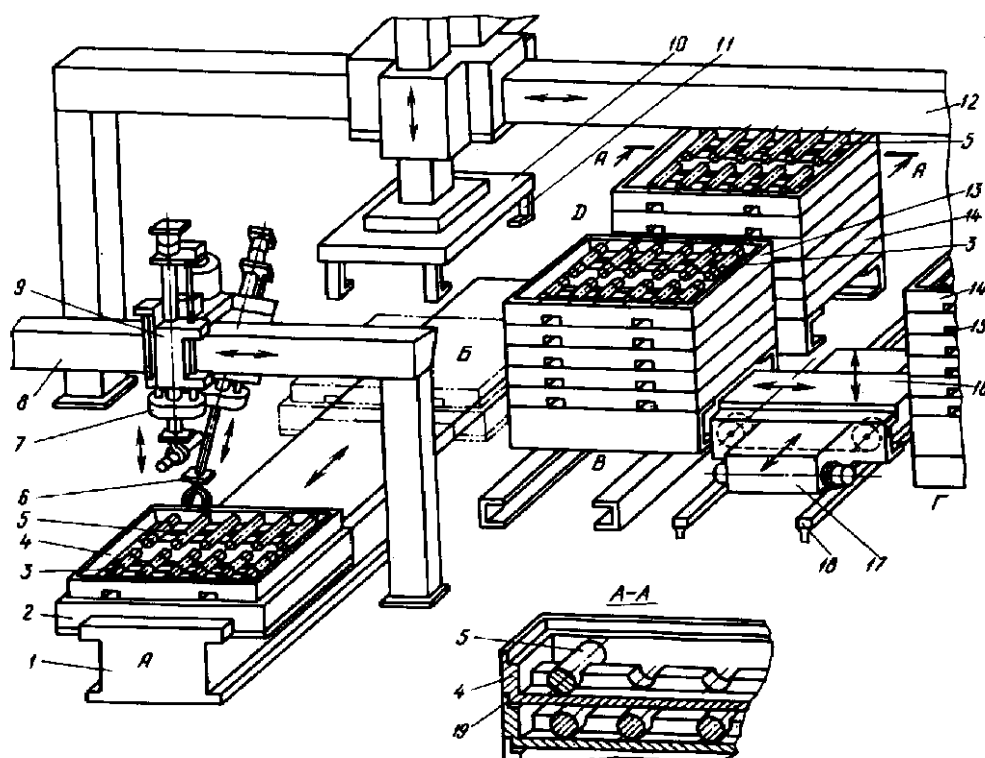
Система накопления заготовок в кассетах (поддонах)
